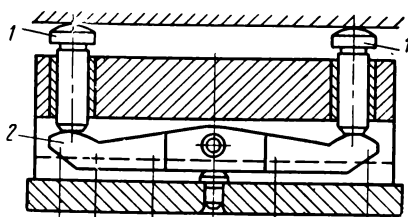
Плавающая самоустанавливающаяся опора с двумя точками контакта
